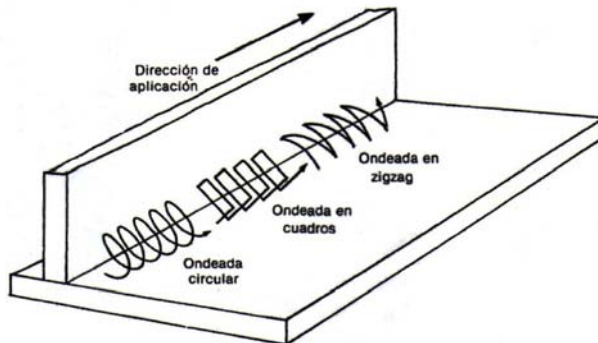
Movimiento de la soldadura ondeada
